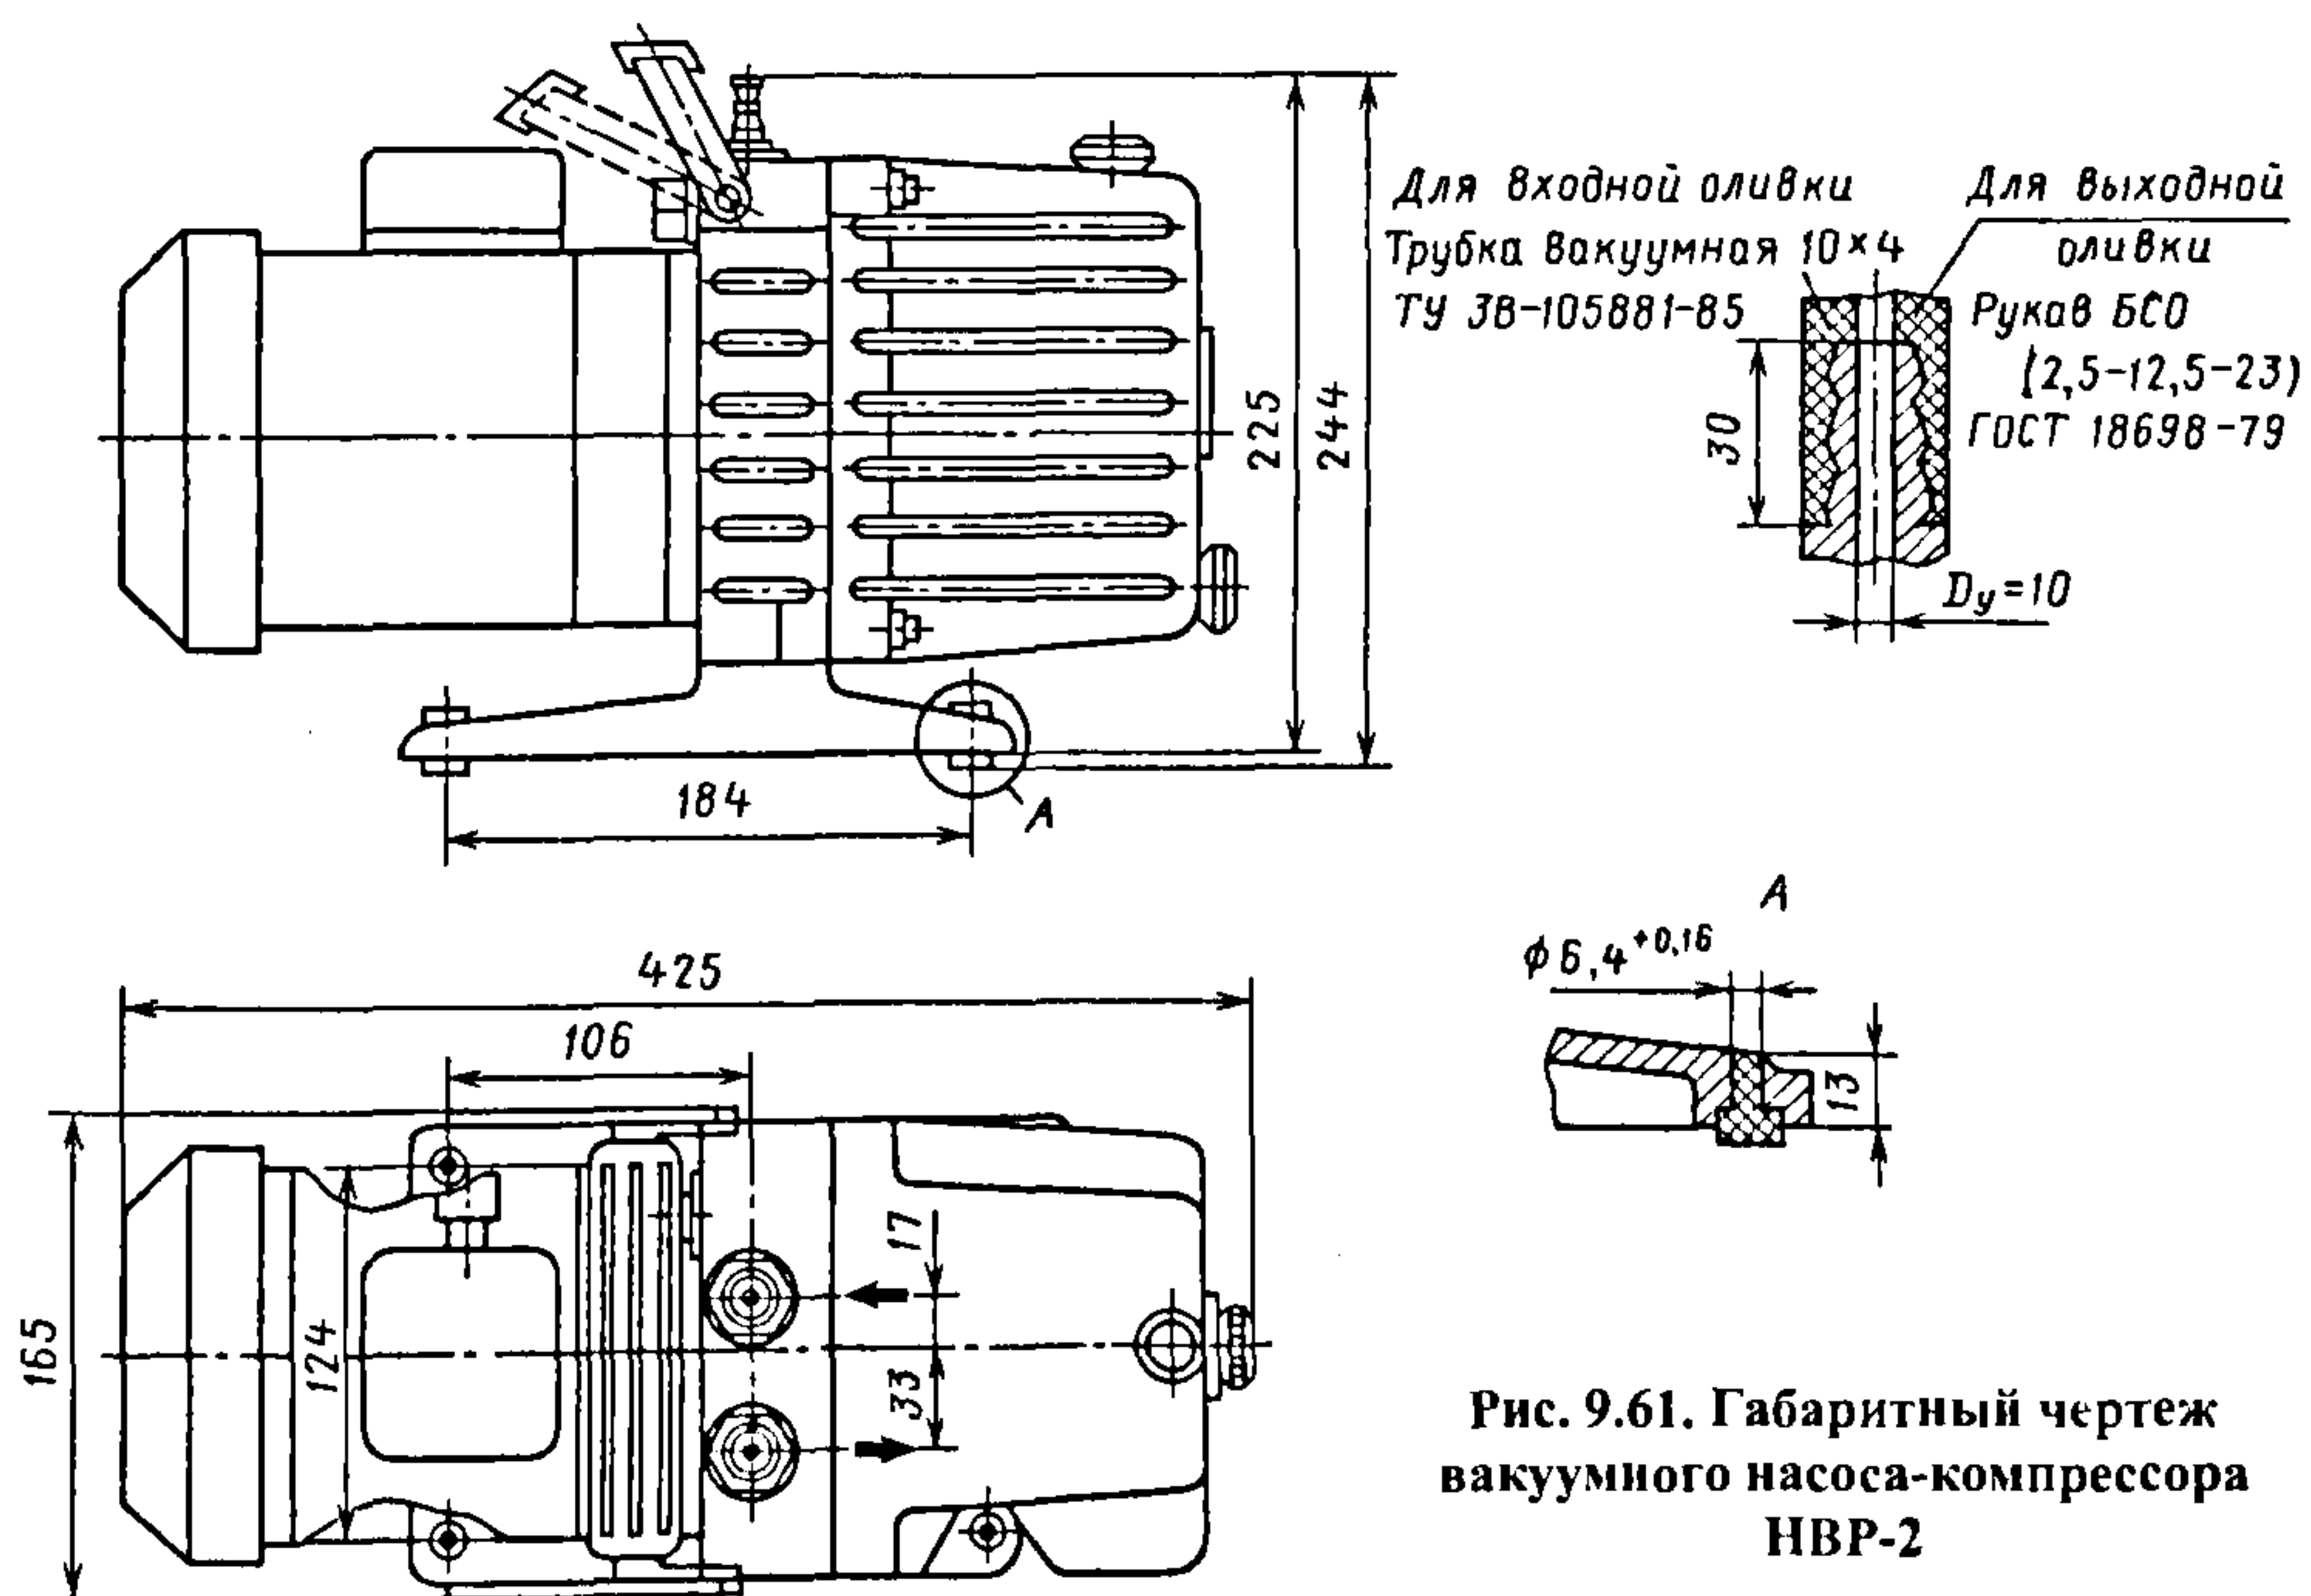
Габаритный чертеж вакуумного насоса-компрессора НВР-2
